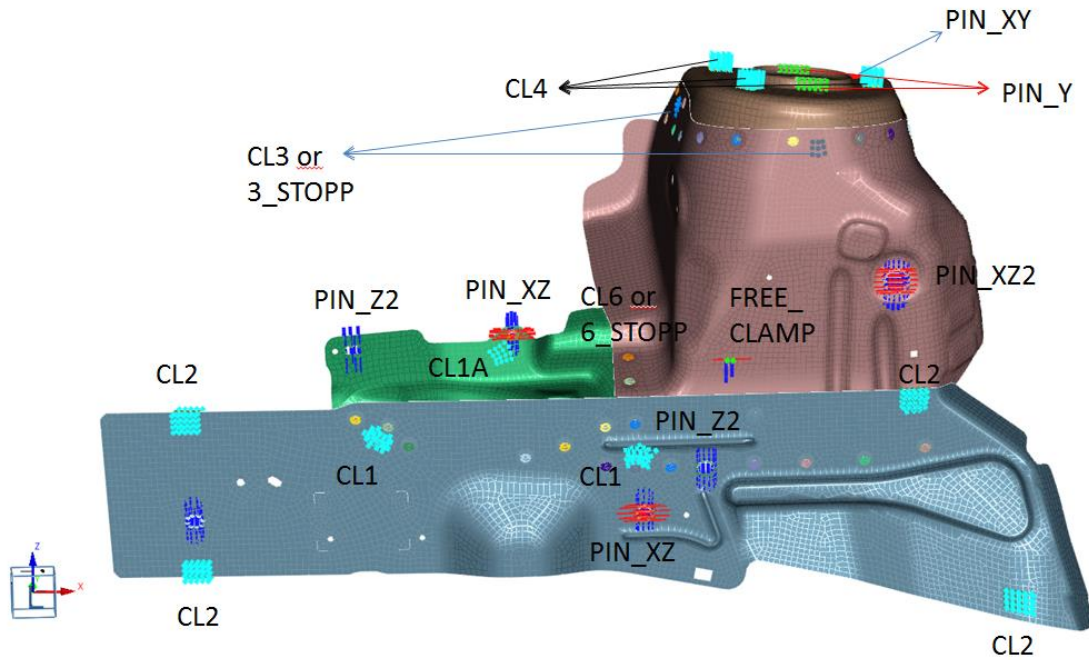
Fikstür ve punta çapı bölgelerini içeren Weld Planner modeli
